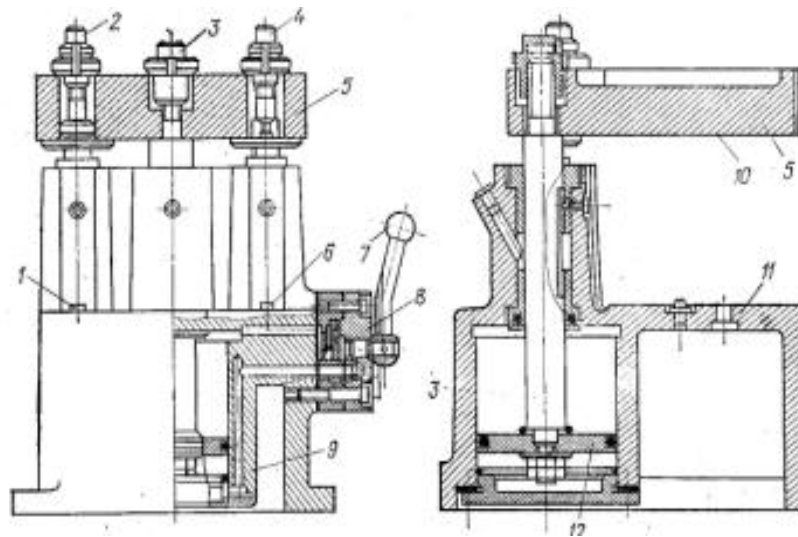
Нормалізований скальчатий кондуктор консольного типу зі вбудованим пневмоприводом
